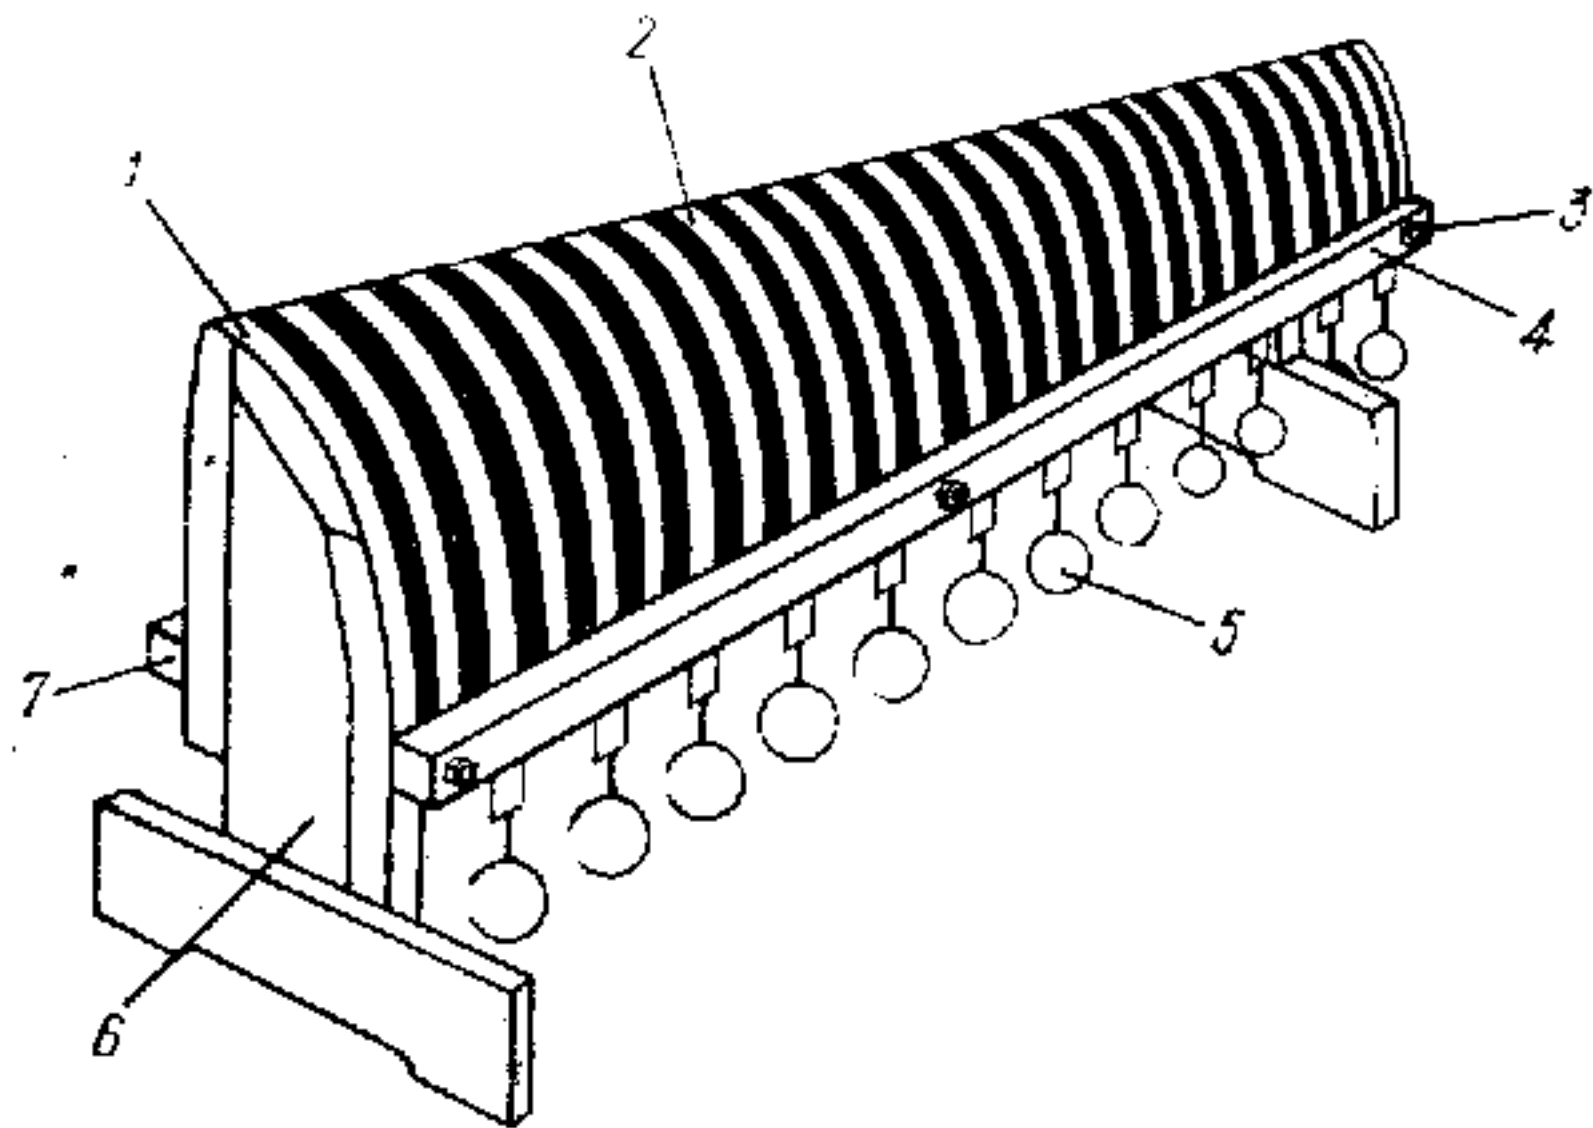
Приспособление для изготовления обшивки носка крыла.
